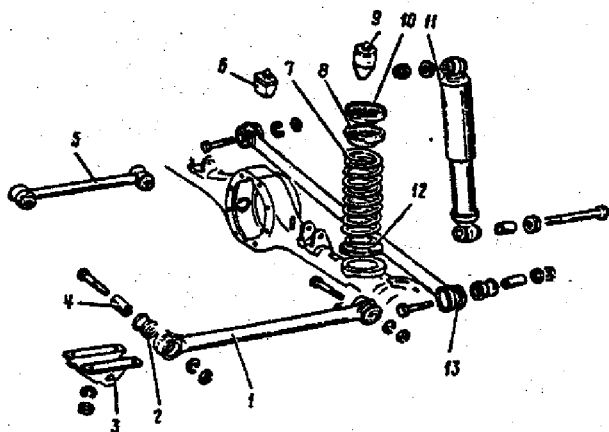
Componentes da suspensão traseira: 1 - barra longitudinal inferior; 2 - bucha de borracha; 3 - suporte; 4 - espaçador; 5 - barra longitudinal superior; 6 - batente complementar; 7 - mola; 8 - apoio da mola; 9 - batente da suspensão; 10 - isolador superior da mola; 11 - amortecedor; 12 - isolador inferior; 13 - barra transversal.
